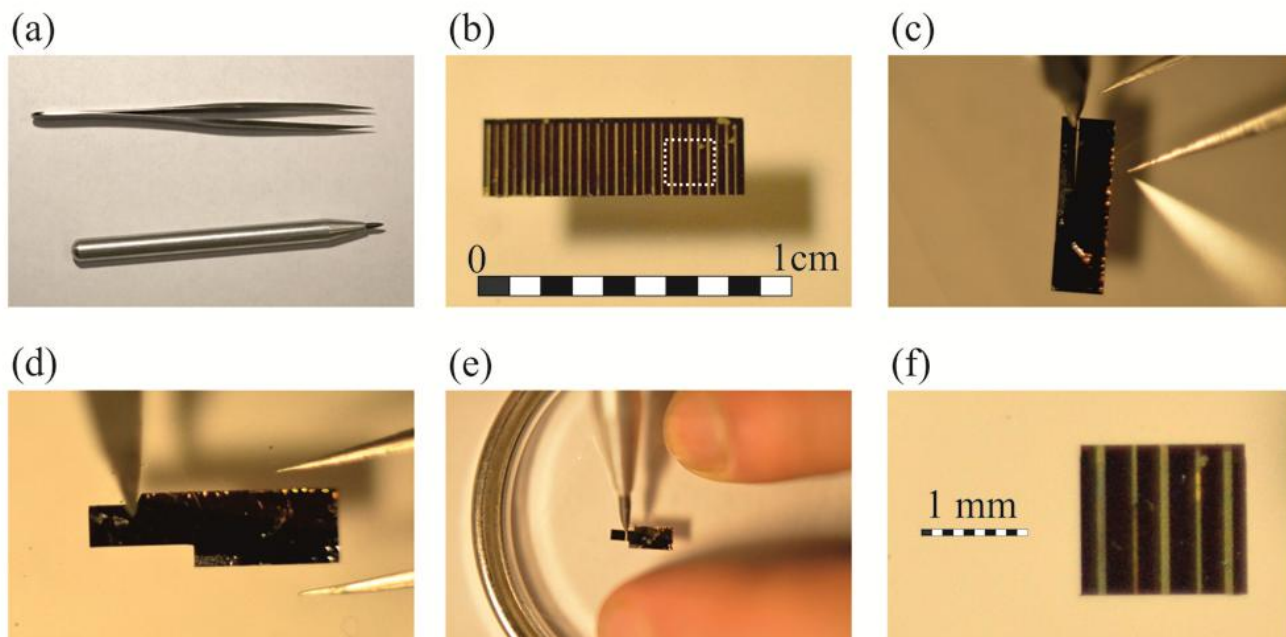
Приготовление чипа с инжекционными лазерами. (а) Победитовый резак и пинцет - инструменты для манипуляции и раскалывания пластины с лазерной гетероструктурой; кадр $100 \times 62 \text{ mm}^2$. (b) Прямоугольный кусочек пластины с 28 полосковыми контактами на лицевой стороне; кадр $13 \times 8 \text{ mm}^2$. (c) Формирование зеркала лазера, пластина лежит лицевой стороной на гладкой стеклянной подставке; кадр $19 \times 12 \text{ mm}^2$. (d) и (e) Выкалывание чипа с 5 контактными полосками; кадры $13 \times 8 \text{ mm}^2$ и $44 \times 27 \text{ mm}^2$. (f) Чип «смотрит» лицевой стороной вверх; кадр $3.7 \times 2.3 \text{ mm}^2$. На (c) и (d), а также (e) пластина прижата к поверхности стекла пинцетом или пальцами через прозрачную лавсановую пленку. Прямоугольная область, выделенная на изображении (b) пунктиром, соответствует чипу на изображении (f). Для фотосъемки использована камера Nikon 3200 и, при необходимости, макрокольцо 31 mm либо линза +6 диоптрий - насадка на объектив Nikkor $50 \text{ mm } f/1.8$. Освещение от светодиодной лампы.
